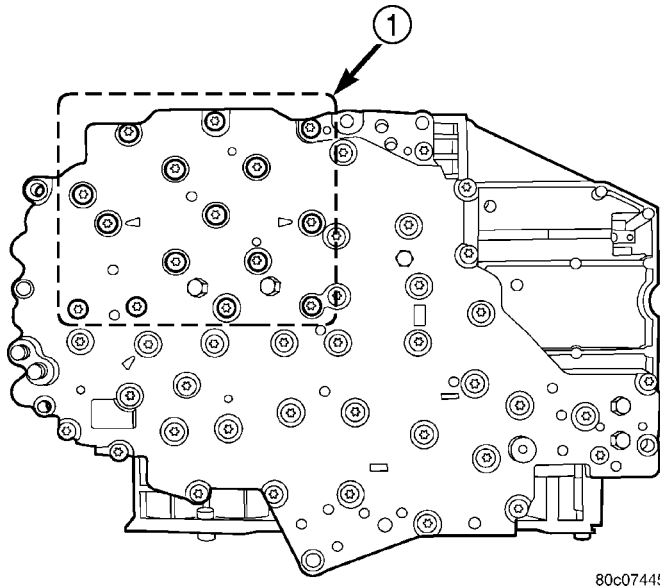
Tornillos del conjunto de TRS/solenoide de la caja de cambios
